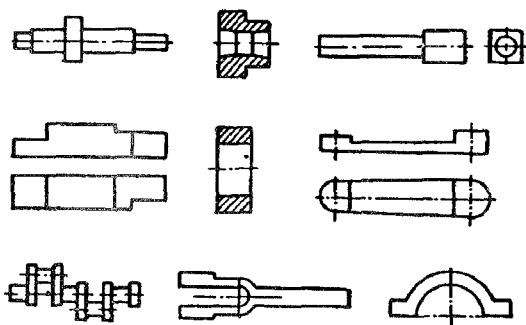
Основные типы заготовок, изготовленных ковкой
